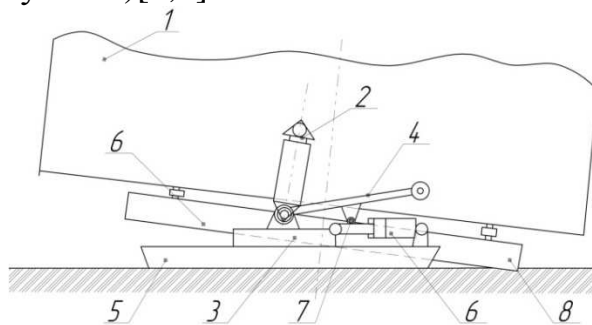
Схема механизма шагания техопорного драглайна: 1 – кузов; 2 – гидроцилиндры подъема; 3 – скользящая опора; 4 – тяга; 5 – опорный башмак; 6 – тяговый гидроцилиндр; 7 – упор; 8 – база.
